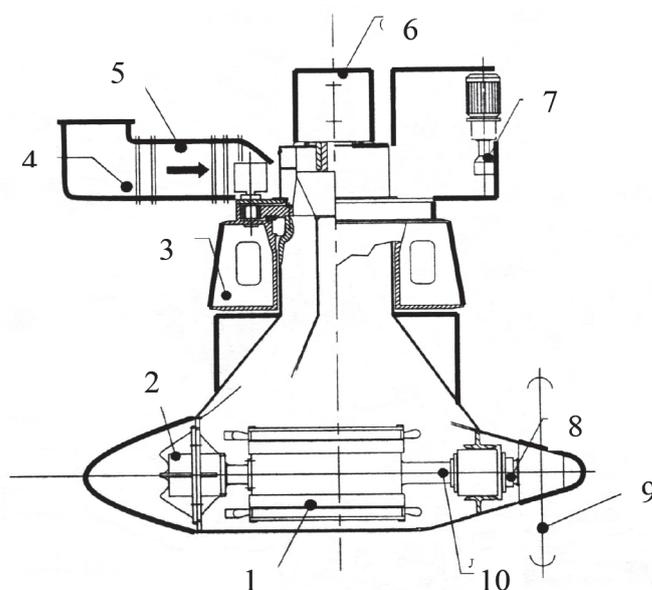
Типовая схема ГВРК с электродвигателем в гондоле: 1 — электродвигатель; 2 — упорный подшипник; 3 — установочный блок; 4 — вентиляционная установка; 5 — воздухоохладитель; 6 — токосъемник; 7 — гидравлическая система поворота колонки; 8 — подшипник и уплотнения гребного вала; 9 — винт фиксированного шага; 10 — гребной вал
